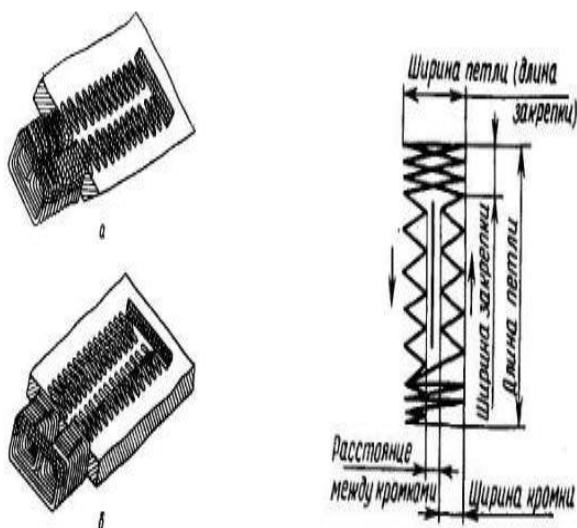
Внешний вид петель и изготовление петли на машине 525 кл.
